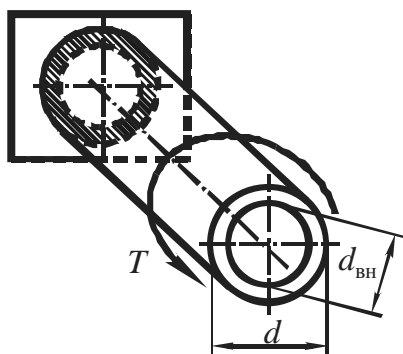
Схема стыкового сварного шва, нагруженного крутящим моментом
